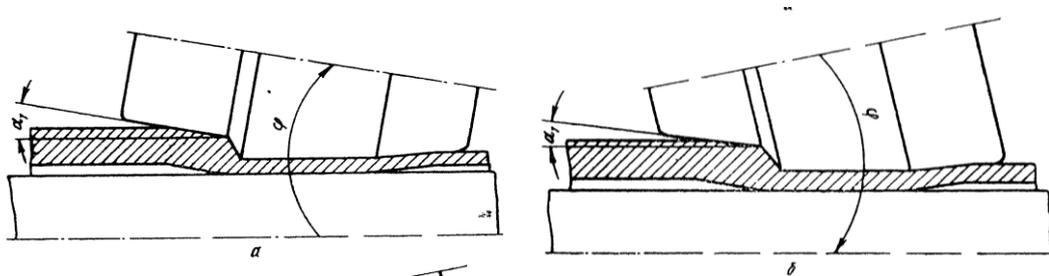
Кут розкочування в трьохвалковому раскатному стані
